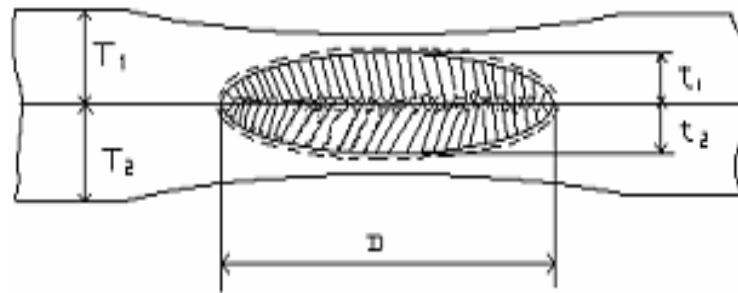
Vista transversal del cupón de prueba de la soldadura.
